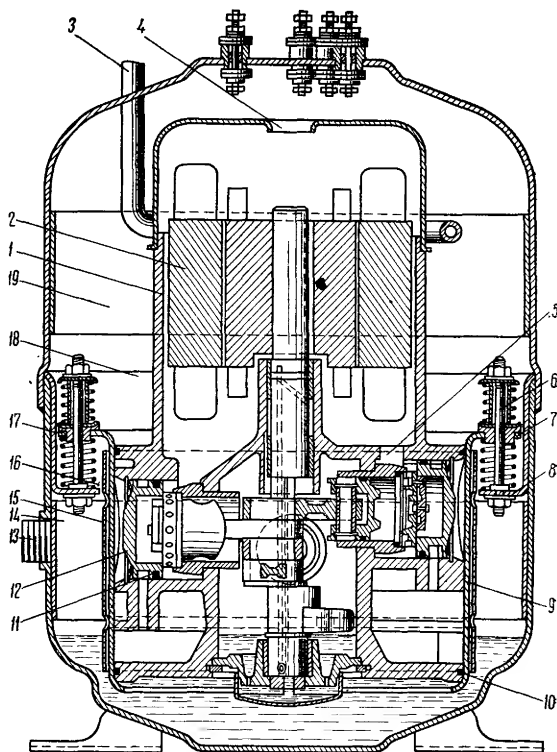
Многоцилиндровый компрессор с внутренним кожухом
